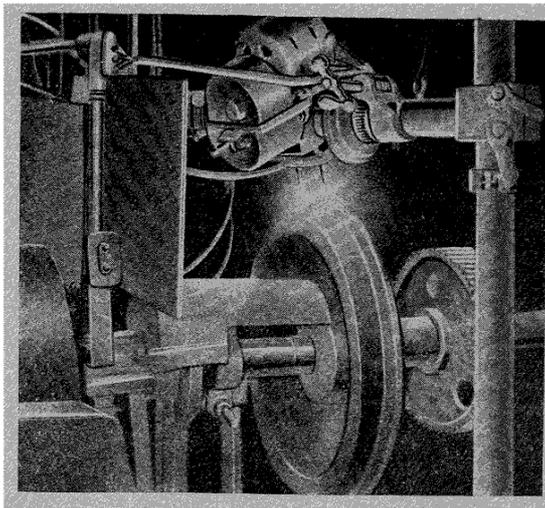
Tête de soudure rechargeant une roue de tramway.
